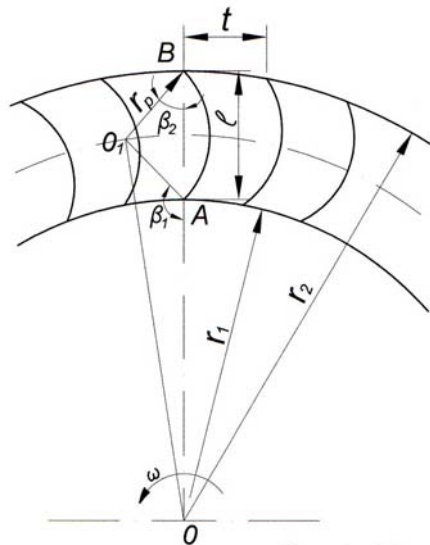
Simbolizarea parametrilor constructivi și de poziționare a paletelor rotorice
